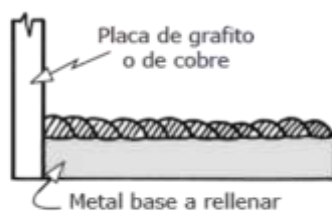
Forma de limitar el relleno de soldadura
